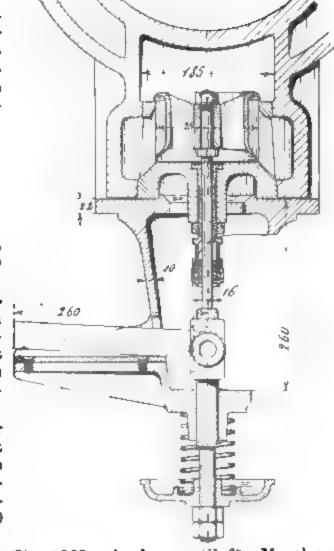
Auslassventil für Maschine von 350 Durchmesser.
